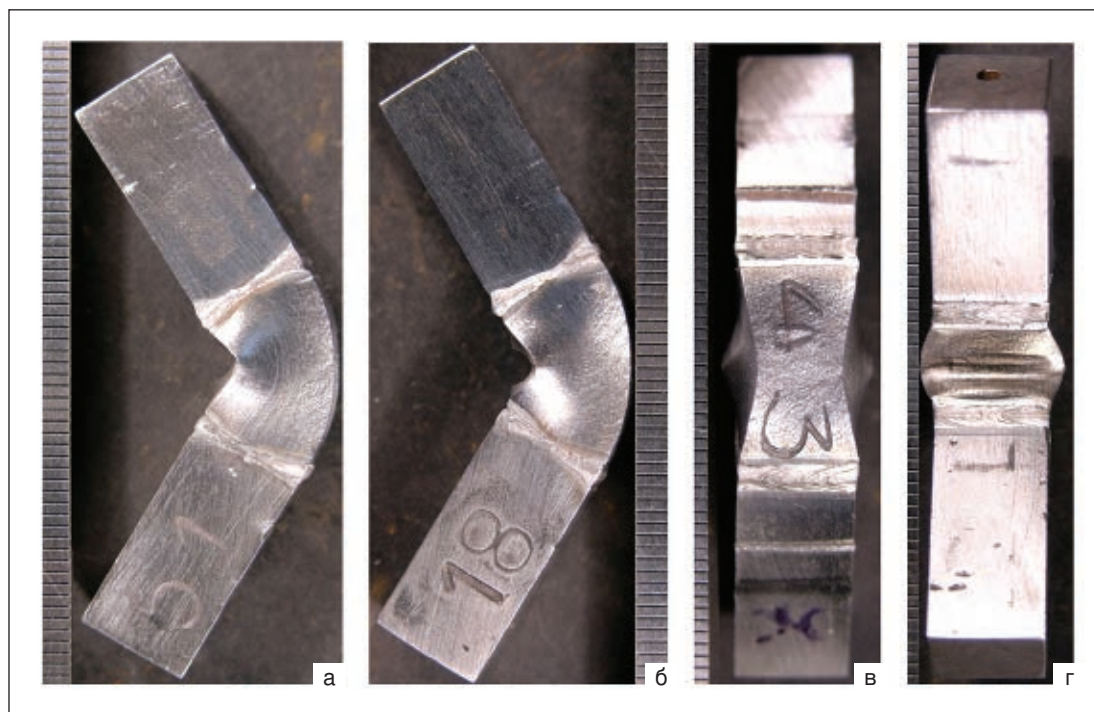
Вид боковых поверхностей образца после квазистатического изгиба на установке Instron 1362 при $T_{исп} = +150^{\circ}\text{C}$, $P_{max} = 34 \text{ кН}$: а, б — боковые поверхности после изгиба; в, г — внешняя и внутренняя (со стороны нагрузки) поверхности
